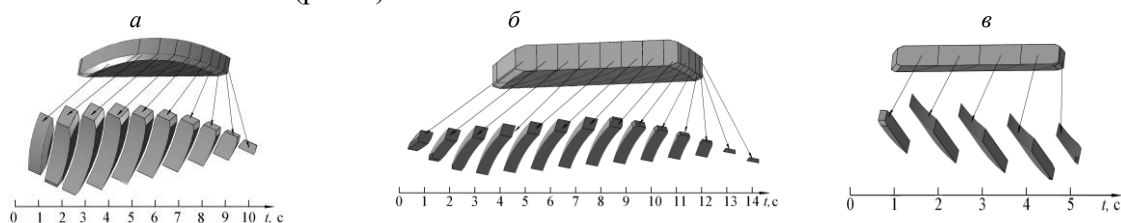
3D - моделювання процесу фрезерування лисок деталі «Палець»:
